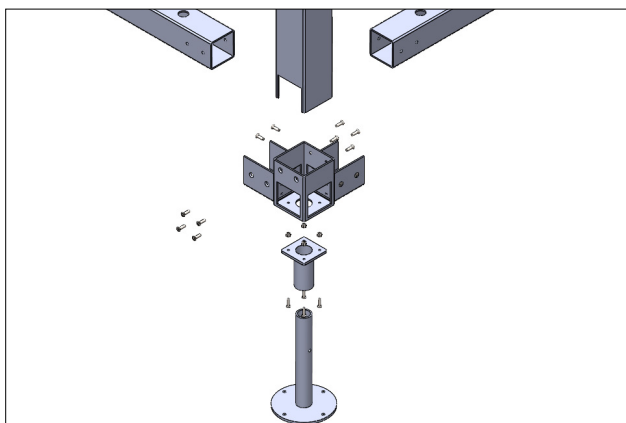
Vista explosionado primer paso de montaje del stand.
